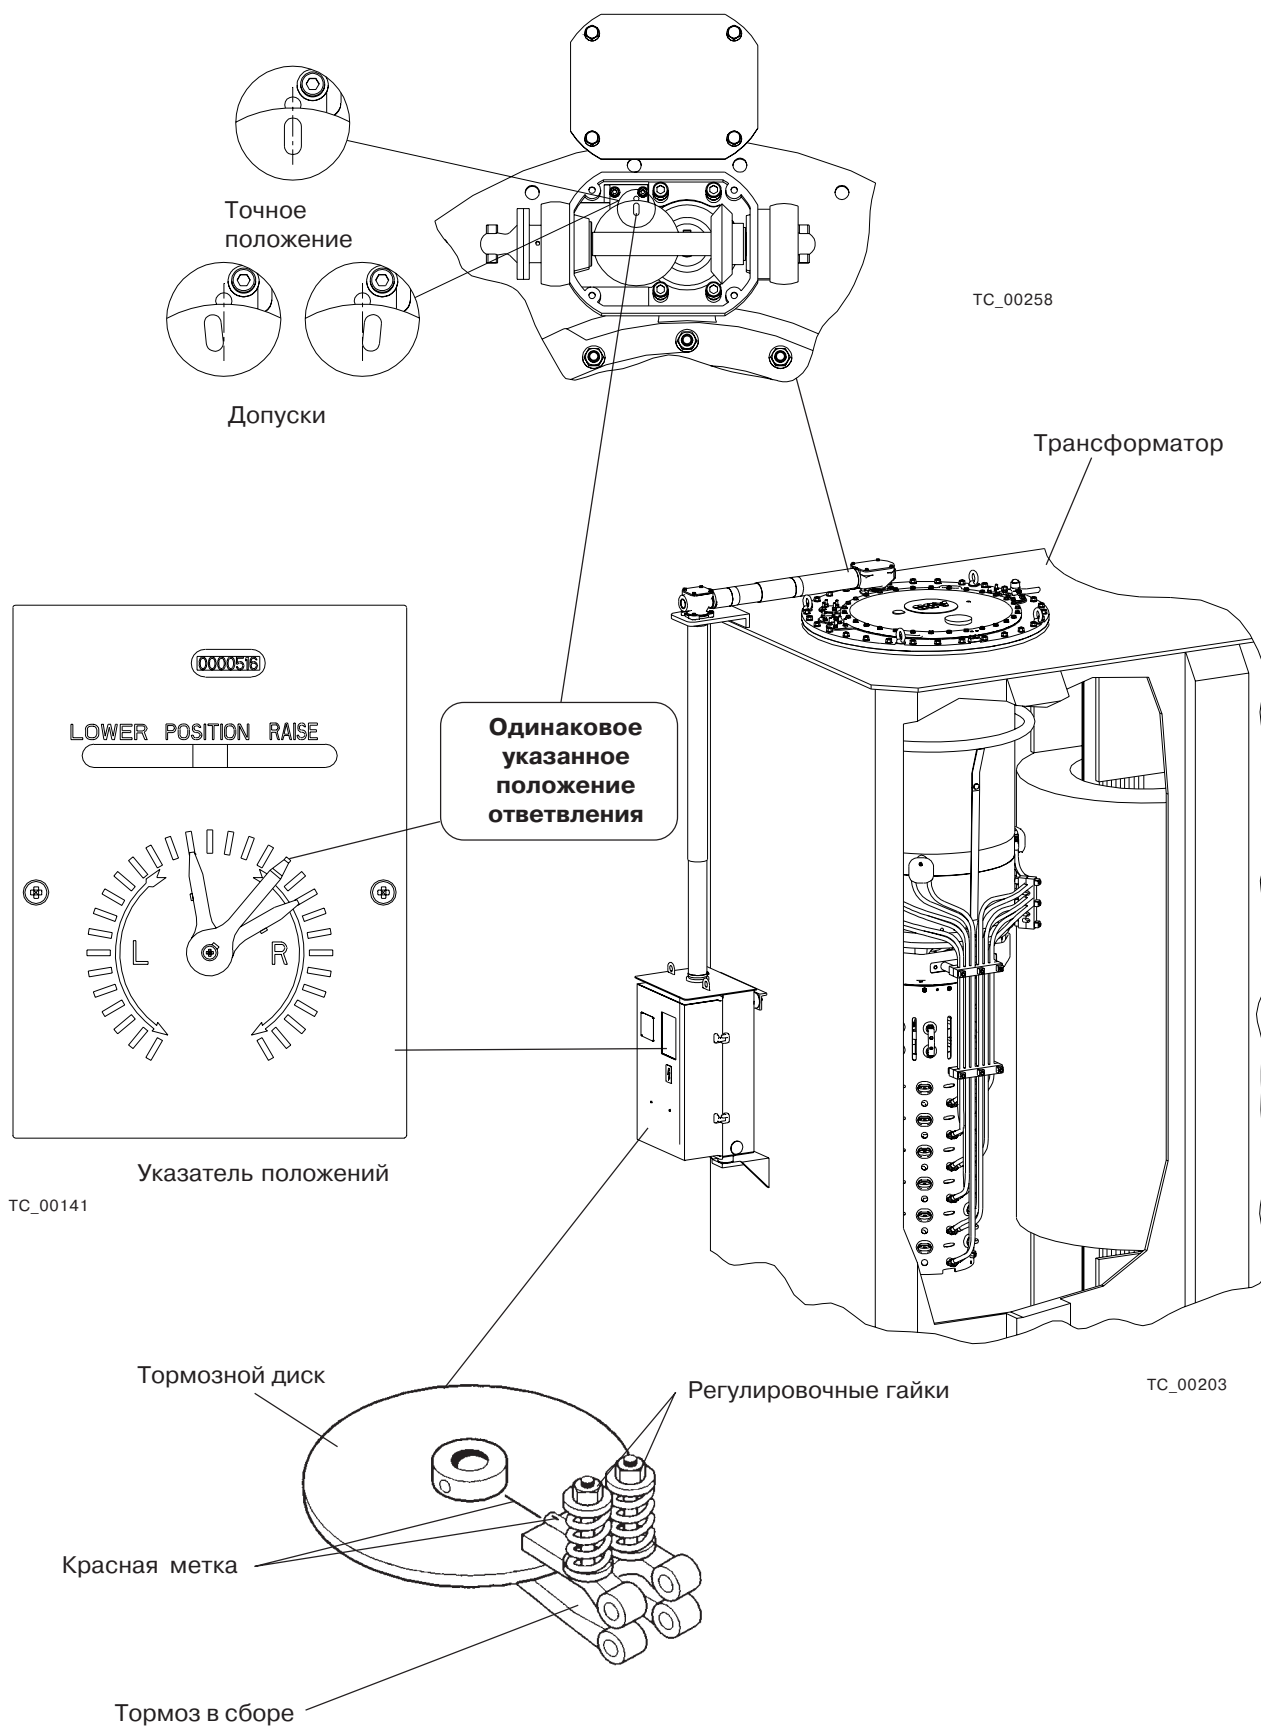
Совмещение положения для устройств UCG, UCL с механизмом моторного привода типа BUE
